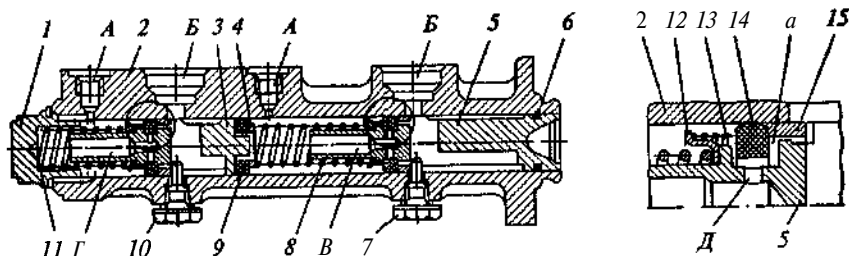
Главный тормозной цилиндр легкового автомобиля ВАЗ: 1 — пробка; 2 — корпус; 3 и 5 — поршни; 4 — шайба; 6, 14 и 15 — кольца; 7 и 10 — ограничители; 8, И и 13 — пружины; 9 — манжета; 12 — тарелка; а — зазор; А, Б и Д — отверстия; В и Г — камеры
